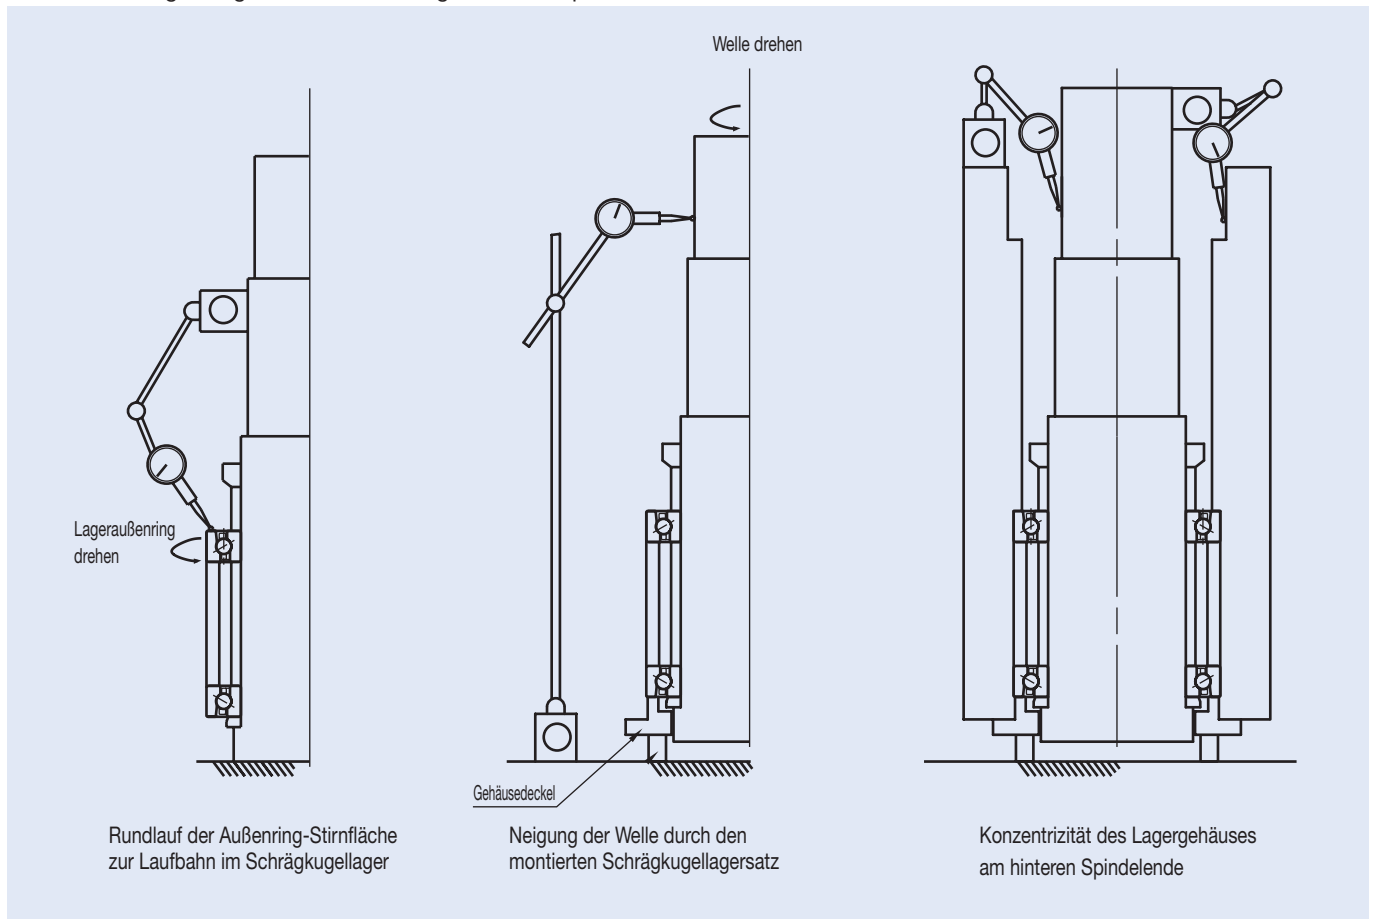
Laufgenauigkeit einer Werkzeugmaschinen spindle
